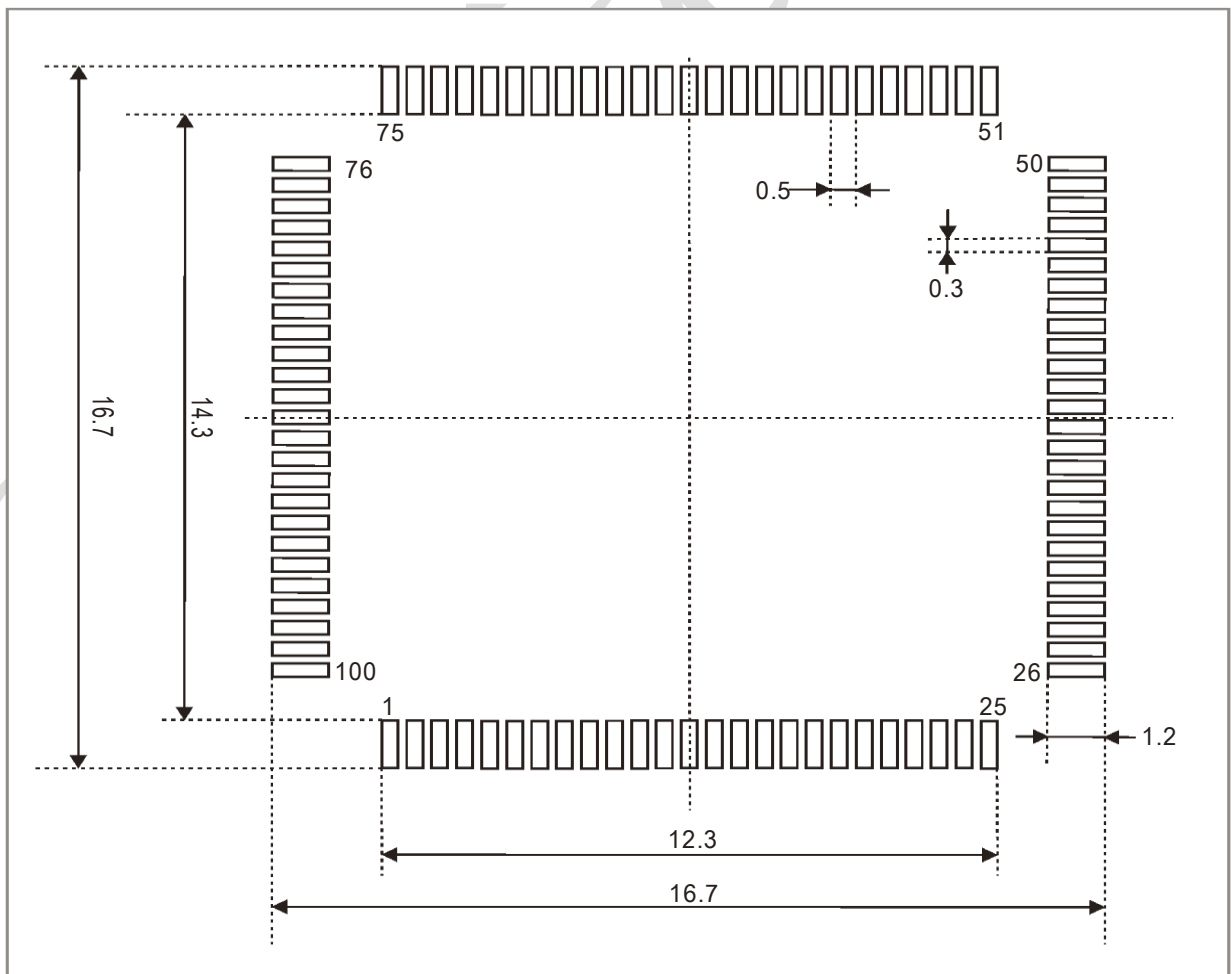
LQFP100 芯片的 PCB 安装尺寸图
